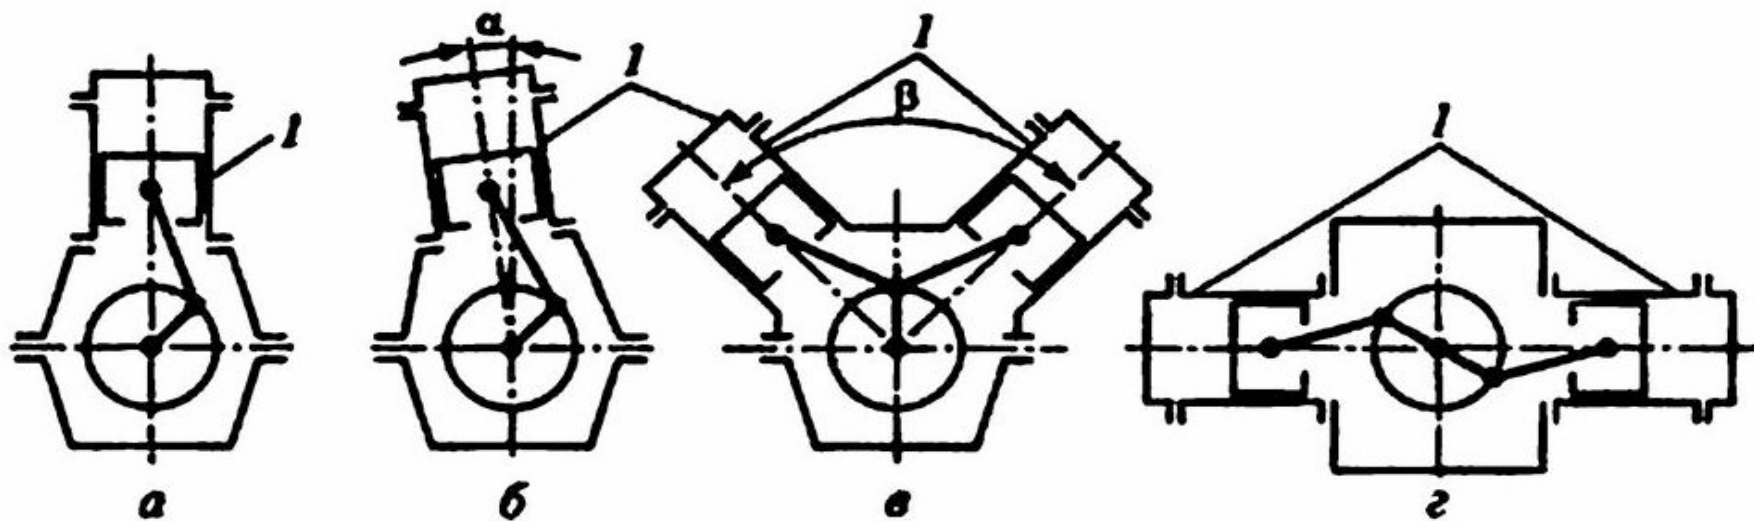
Схемы компоновки цилиндров двигателей:
